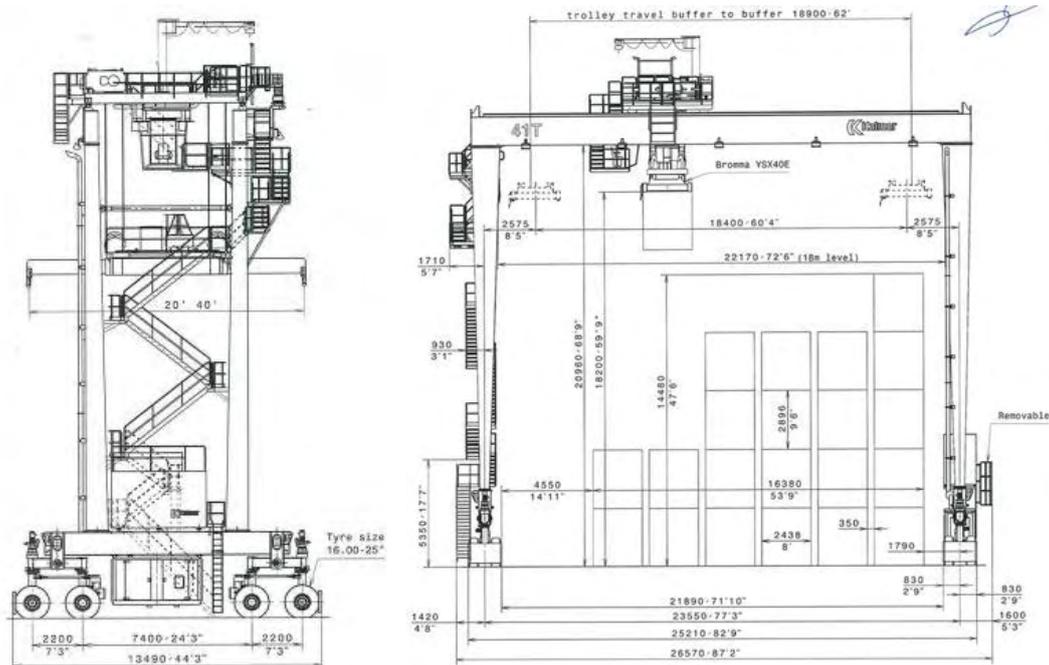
Configuração exemplificativa de pórtico de parque eRTG (vista lateral e de frente, respetivamente)
